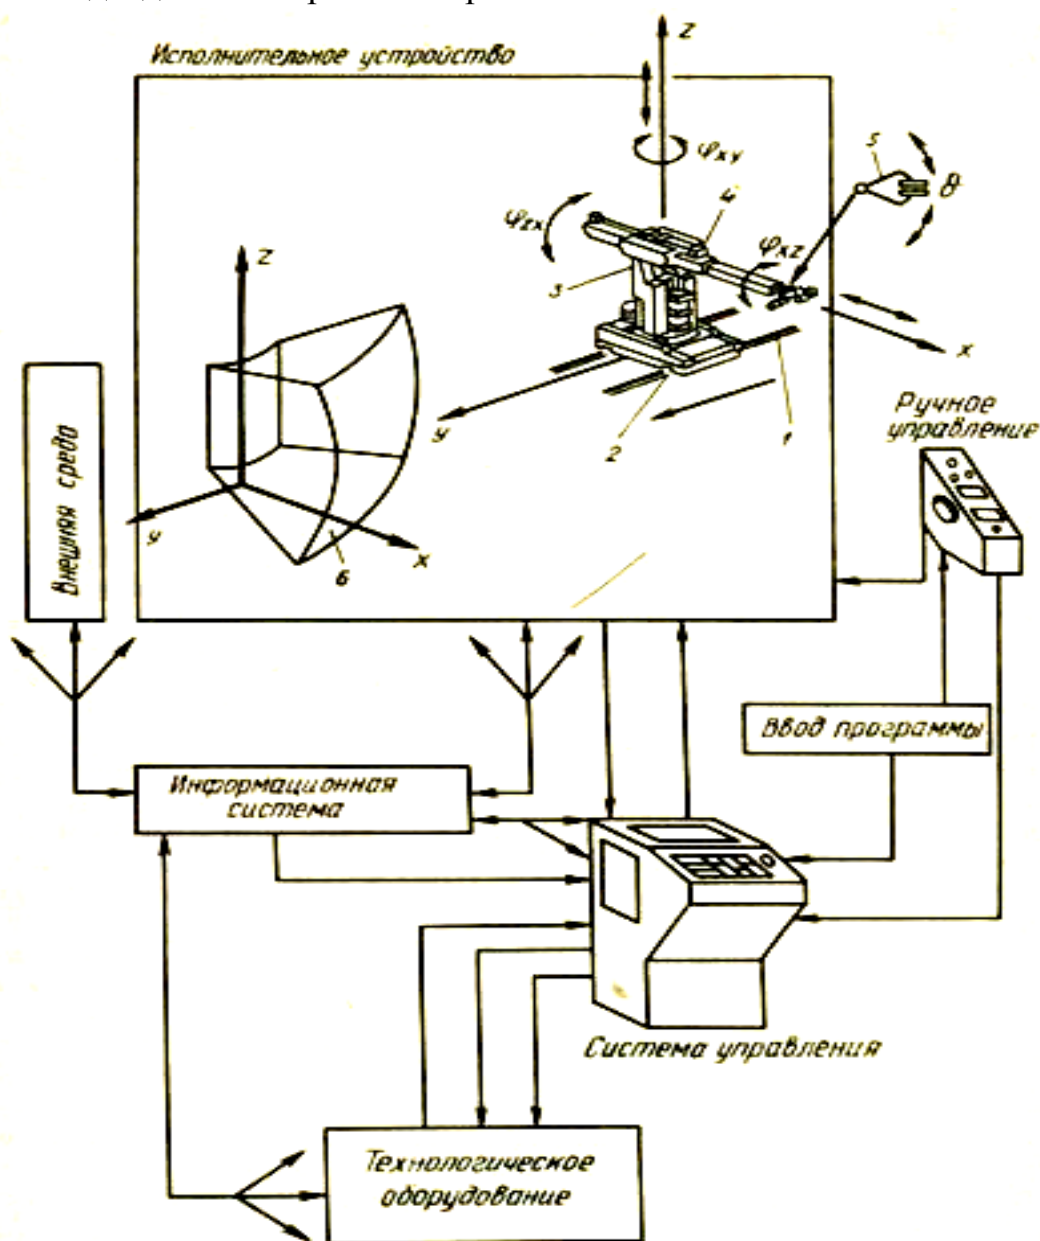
Структурная схема ПР, основные элементы конструкции и виды движений рабочих органов: 1 – трос; 2 – основание; 3 – корпус; 4 – рука; 5 – захватное устройство; 6 – рабочая зона и система координат основных движений ПР; δ – направление движения зажима (захватывания) детали; δ и φ_{xz} – ориентирующие движения; XX , ZZ , φ_{xy} , φ_{xz} – транспортирующие движения; XY , ZX – координатное движение
